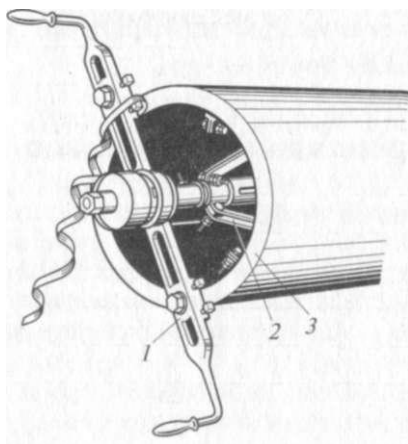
Ручное приспособление для торцовки и снятия фасок на концах труб:
